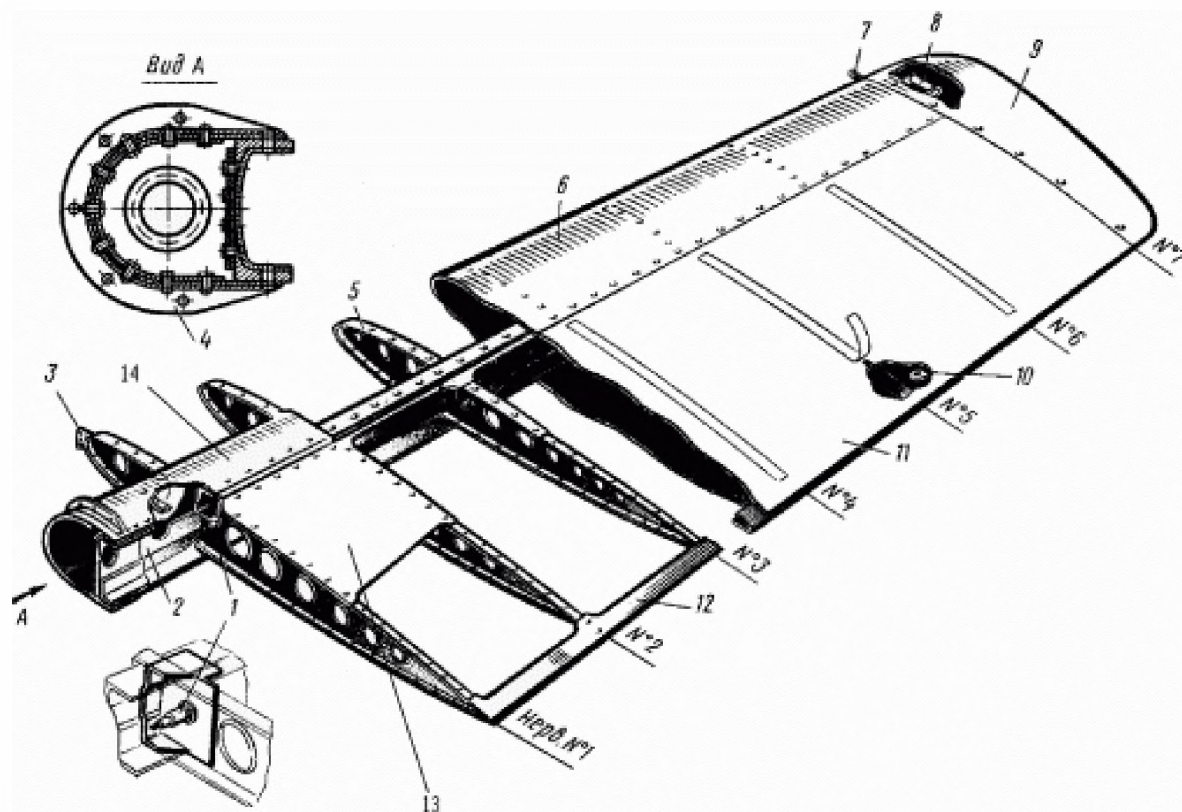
Каркас консоли стабилизатора вертолета Ми-8 [8]:
